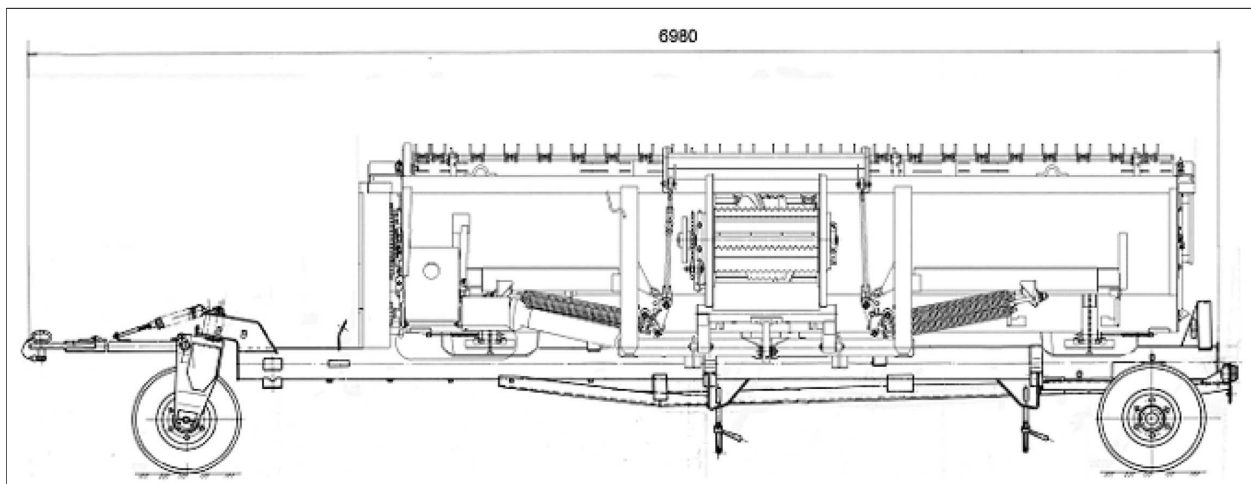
Схема установки жатки на тележку (вид слева)
